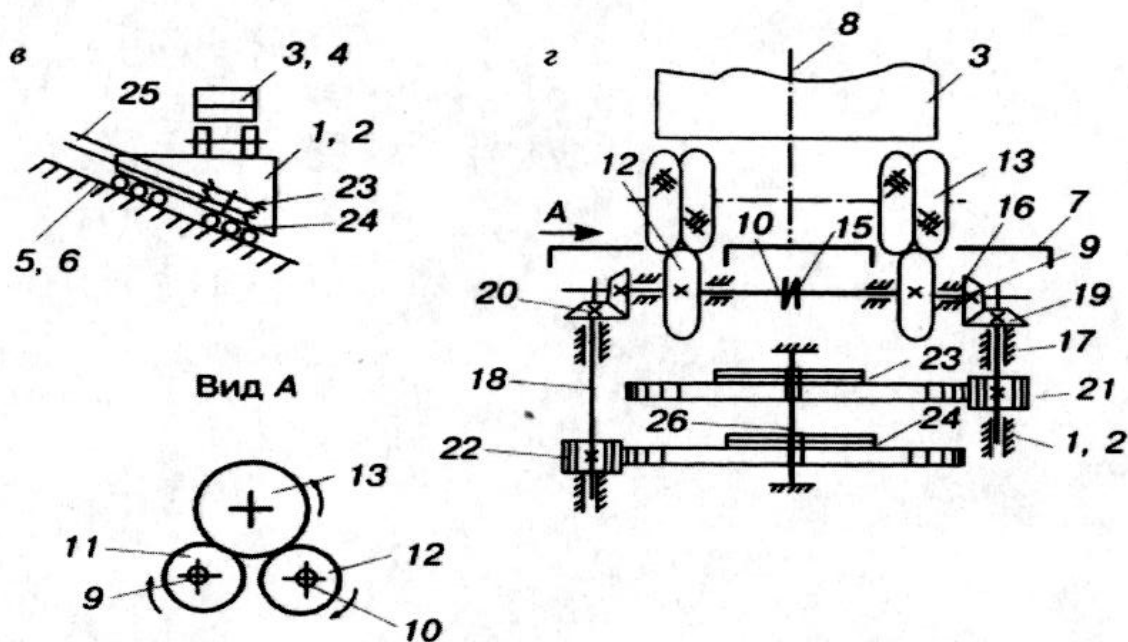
б – план; в – вариант поперечного размещения самосвала на тележке; г – кинематическая схема привода канатных блоков;
